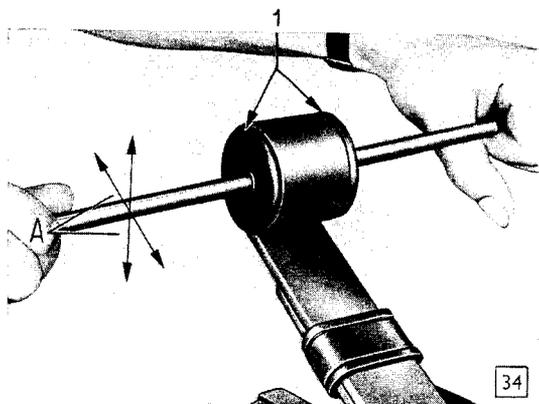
Einteilige Gummibuchse mittig zum Federauge ausrichten
